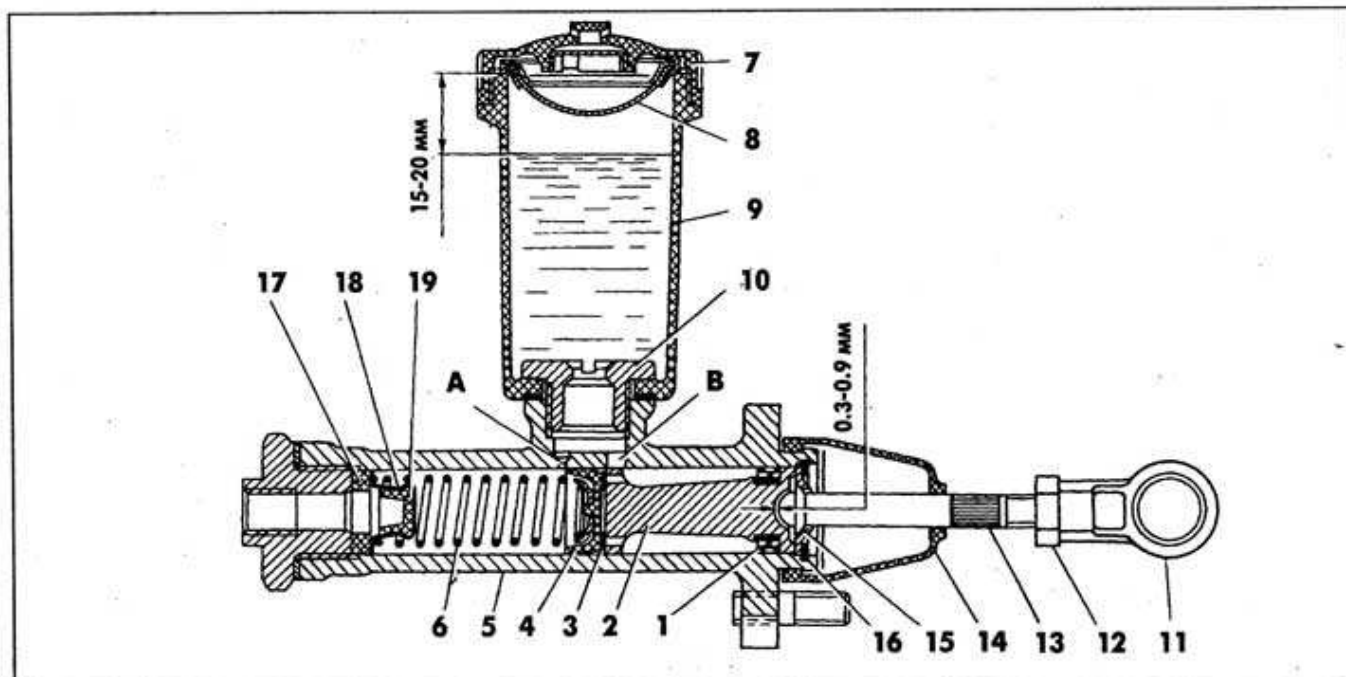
Главный цилиндр привода выключения сцепления:
